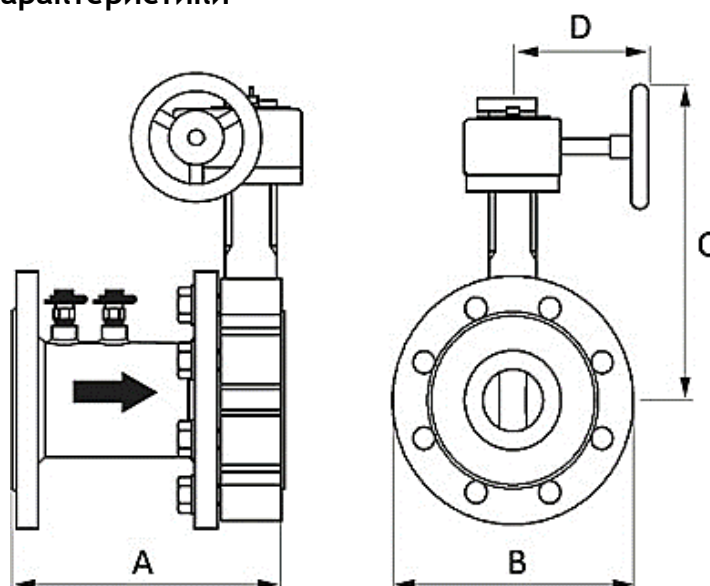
Габаритные размеры NexusValve Fluctus FODRV с измерительными ниппелями
